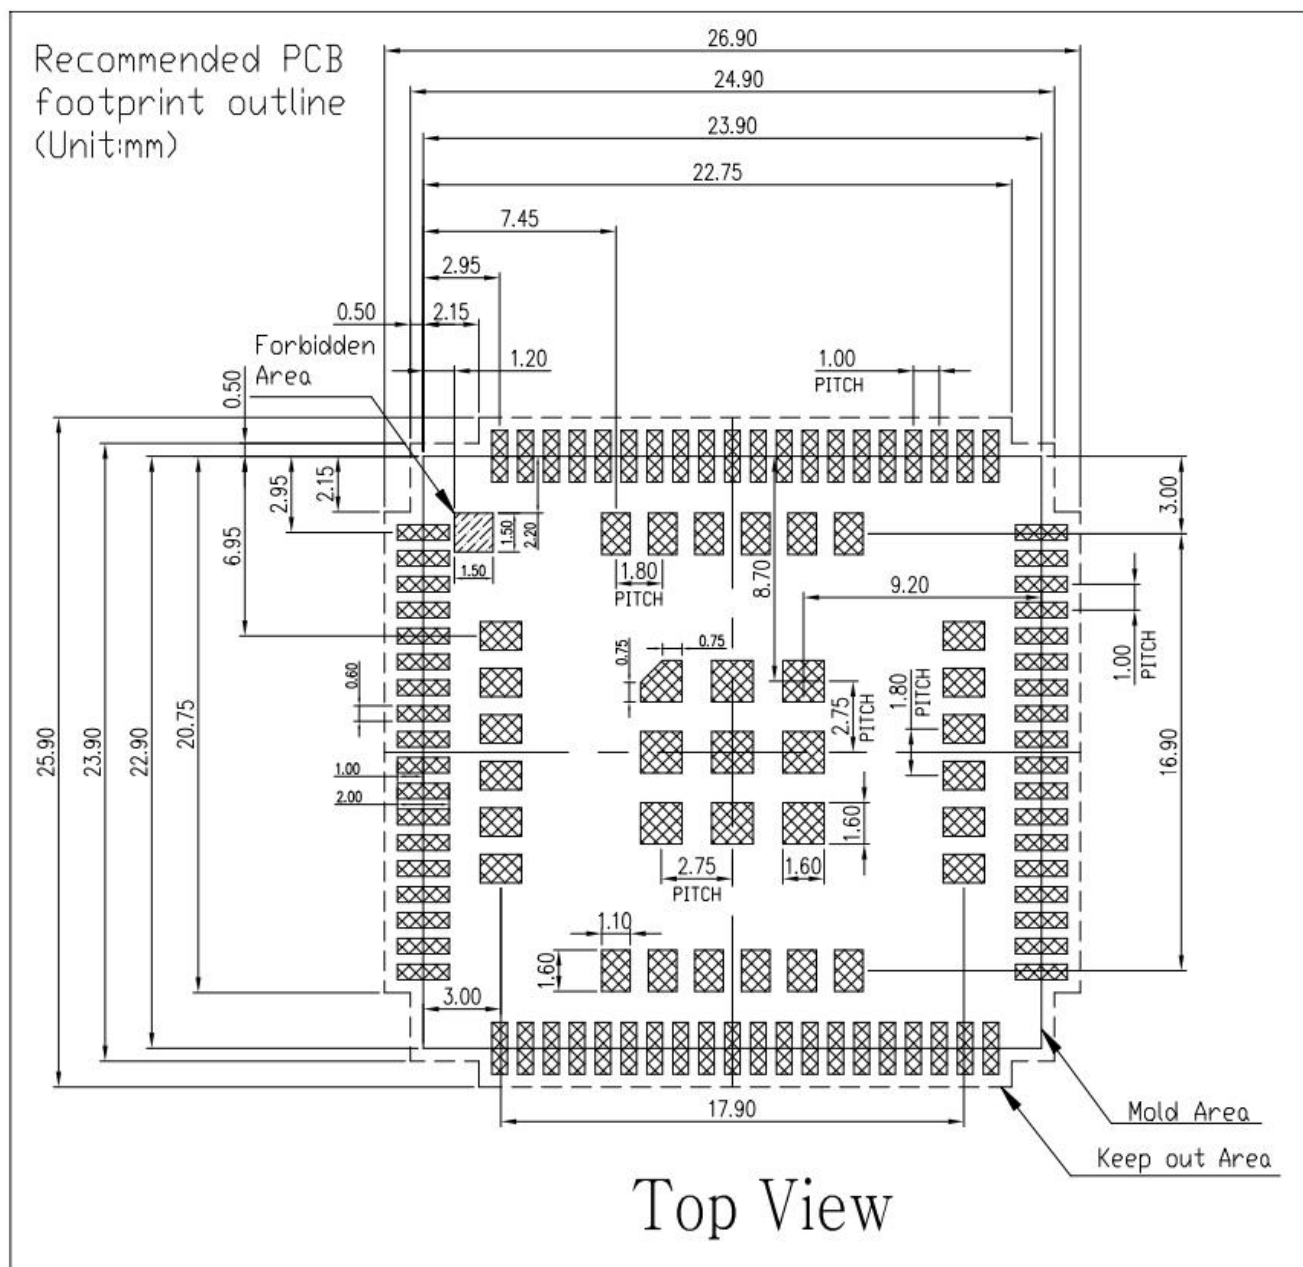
推荐 PCB 封装尺寸 (单位: 毫米)
